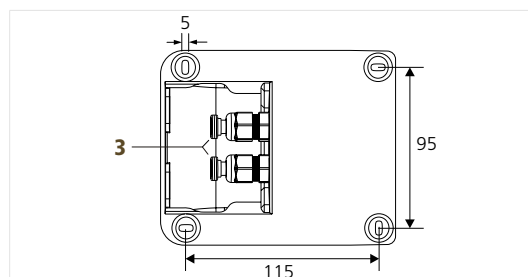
Abmessungen für Montagelöcher Sockel (Angaben in mm)
